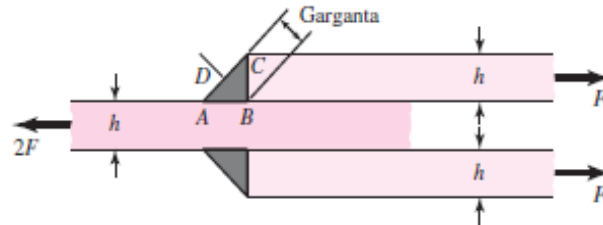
Soldadura con filetes transversales, Elaborado por: G. Quintana, J. Ruales
